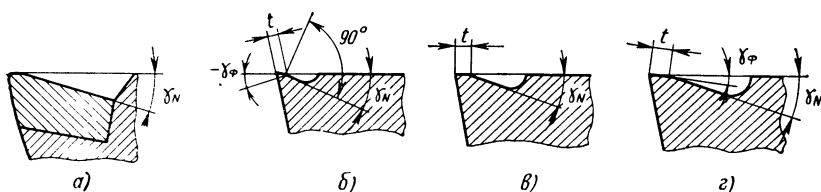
Формы заточки передних поверхностей резцов из инструментальных сталей
